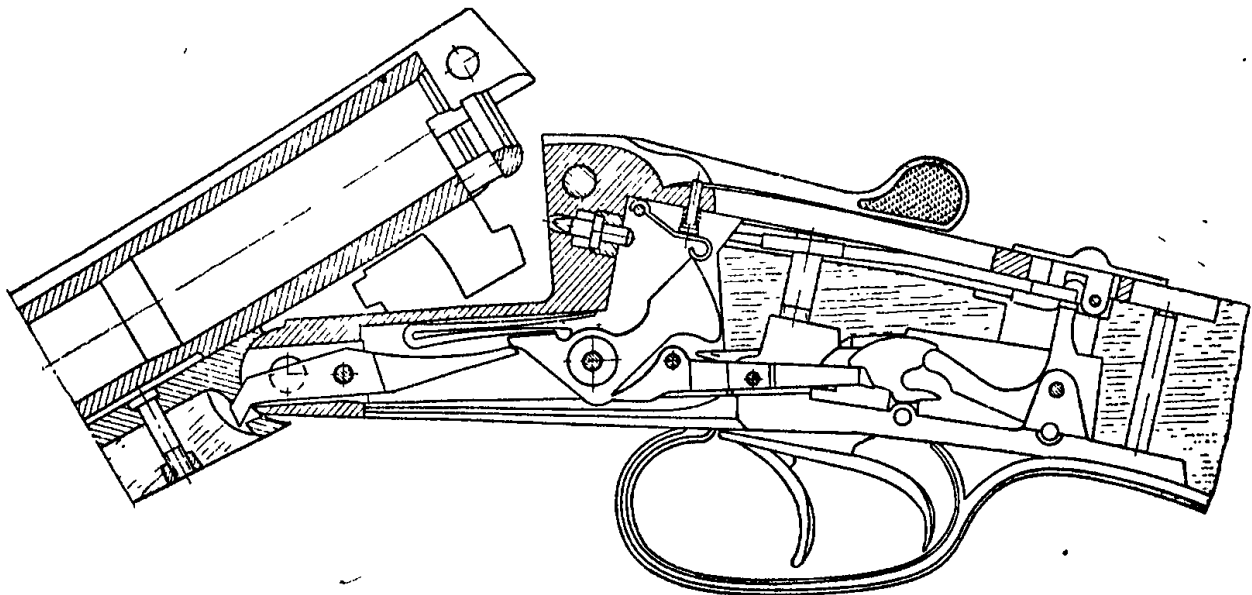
Схема расположения деталей ударного механизма, смонтированного в коробке ружья «ИЖ-54»
